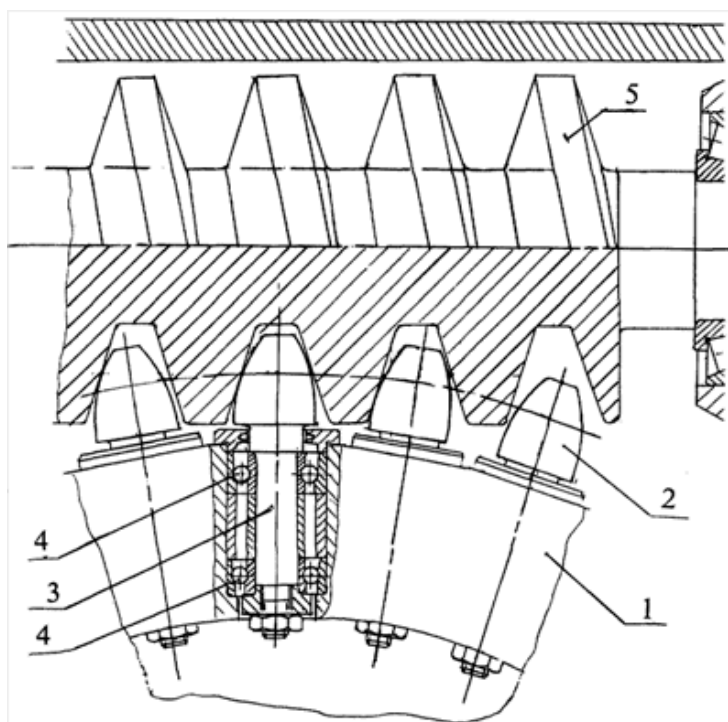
Червячная передача: 1 - корпус червячного колеса; 2 – ролики; 3 – ось ролика; 4 – подшипники.
